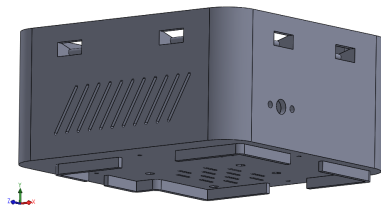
Posición inicial de impresión del cuerpo principal.
